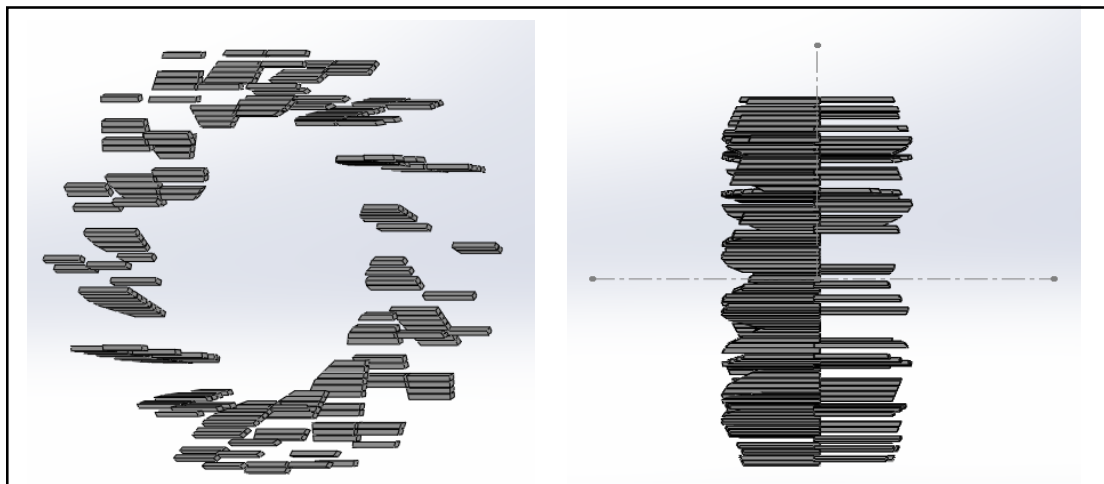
Les barres de poussière qui généreront le déséquilibre.
